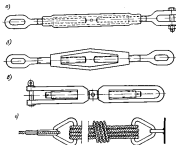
Типы талрепов: а — закрытый; б — открытый; в — с отверстием втулки; г — тросовый
